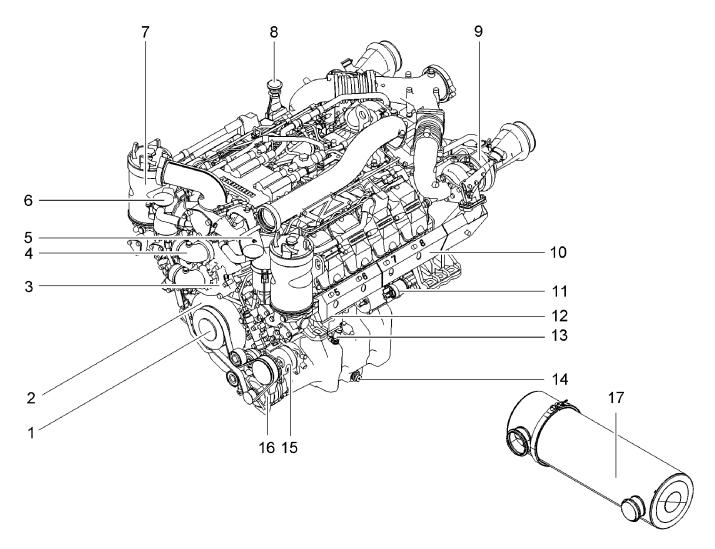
Componentes del motor diésel / Vista desde la izquierda
